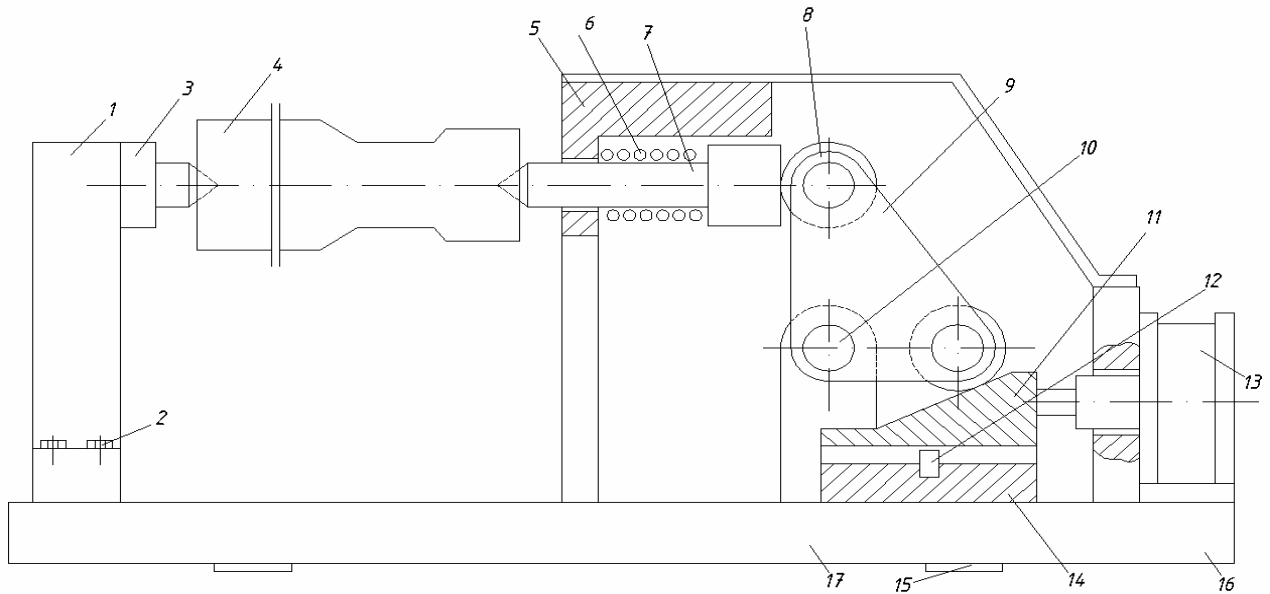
Приспособлення для фрезерування двох пазів
